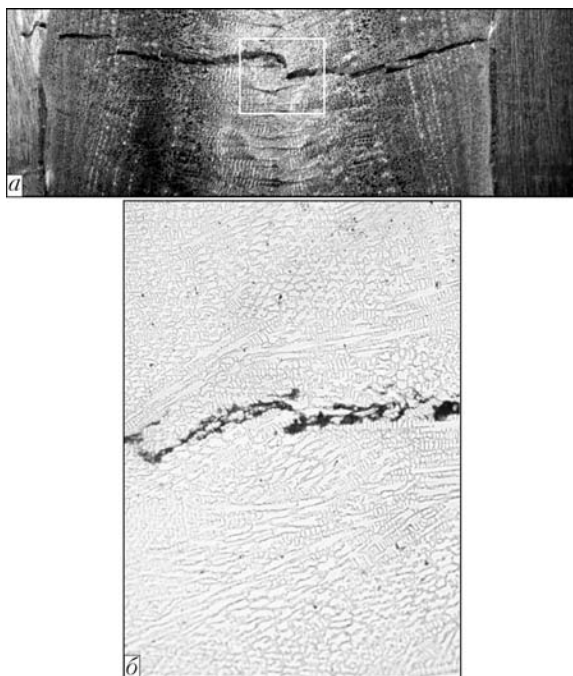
Поверхность сварного соединения (а), $\times 25$ и микроструктура металла шва (б), $\times 200$
